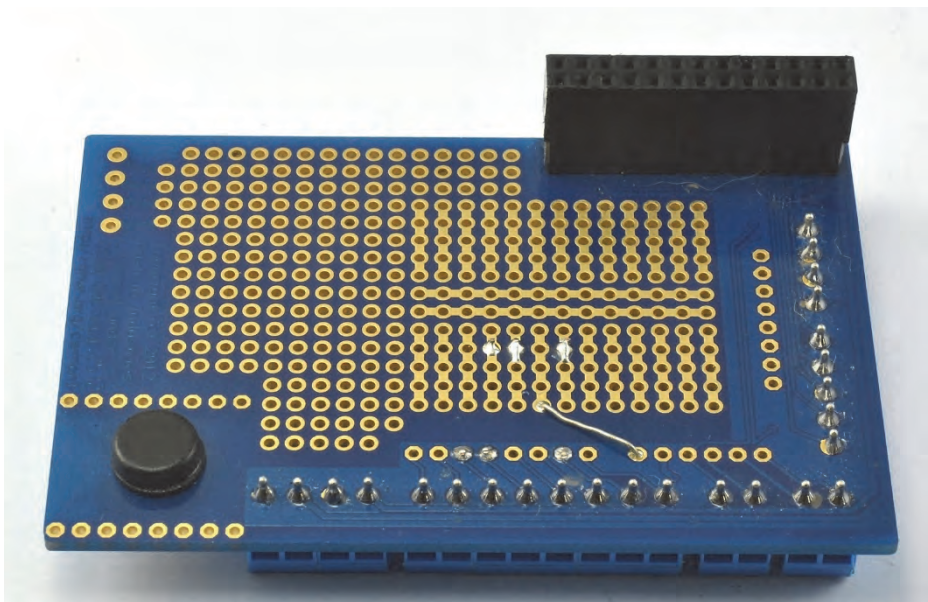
Soldar enlace de cable a la placa de prototipado para Pi.
